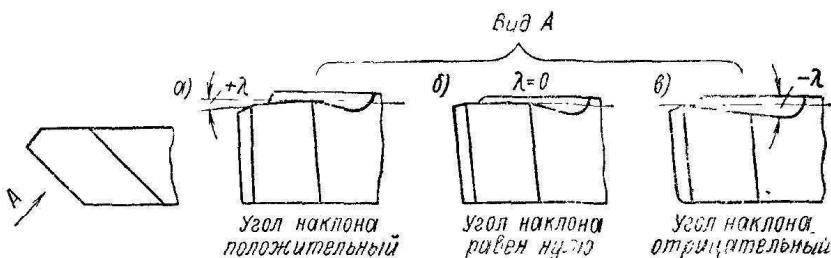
Углы наклона главной режущей кромки: положительный (а), равный нулю (б) и отрицательный (в)
